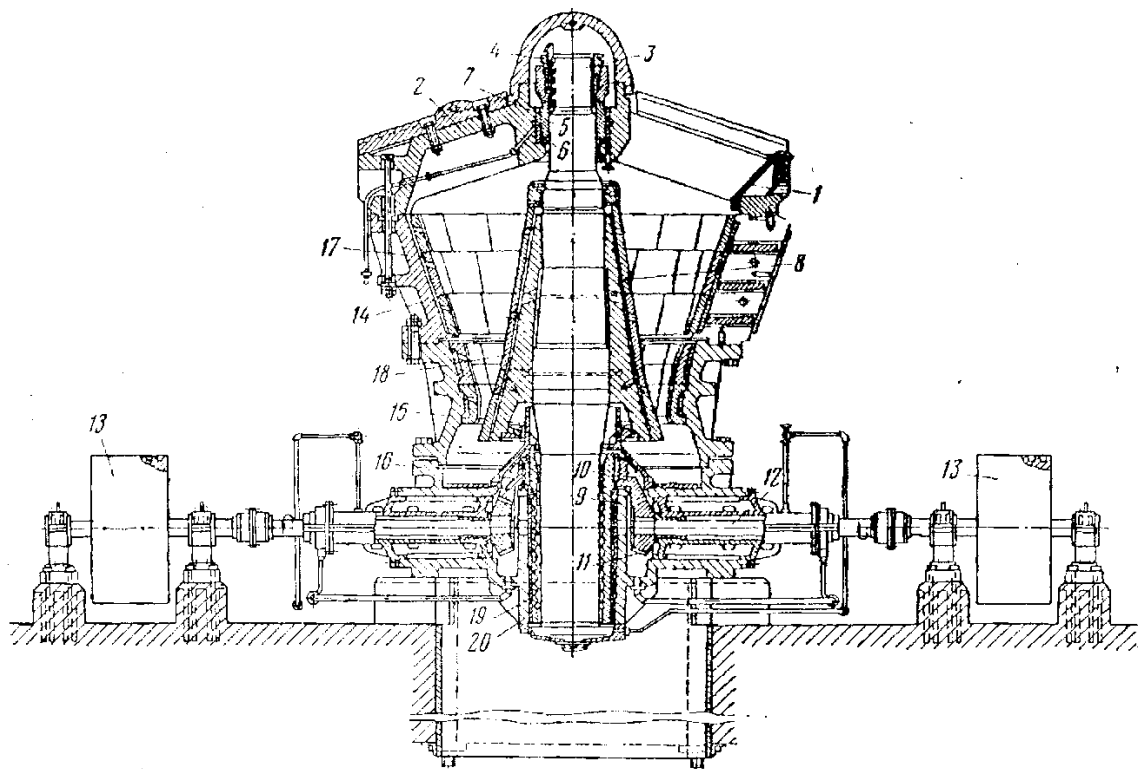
Загальна конструкція конусної дробарки крупного дроблення ККД-1500/180: 1, 14, 15 – пояс (кільця), 2 – траверса, 3 – вал головний, 4 –
